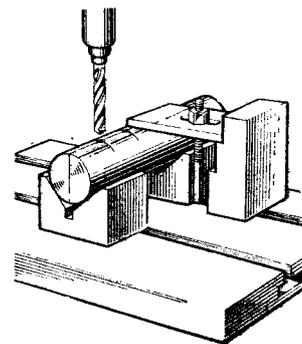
Закрепление цилиндрической детали в призмах с применением прижимных планок
